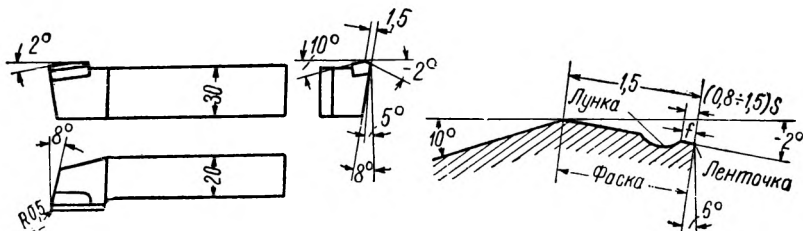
Подрезной резец конструкции Г. С. Борткевича.
